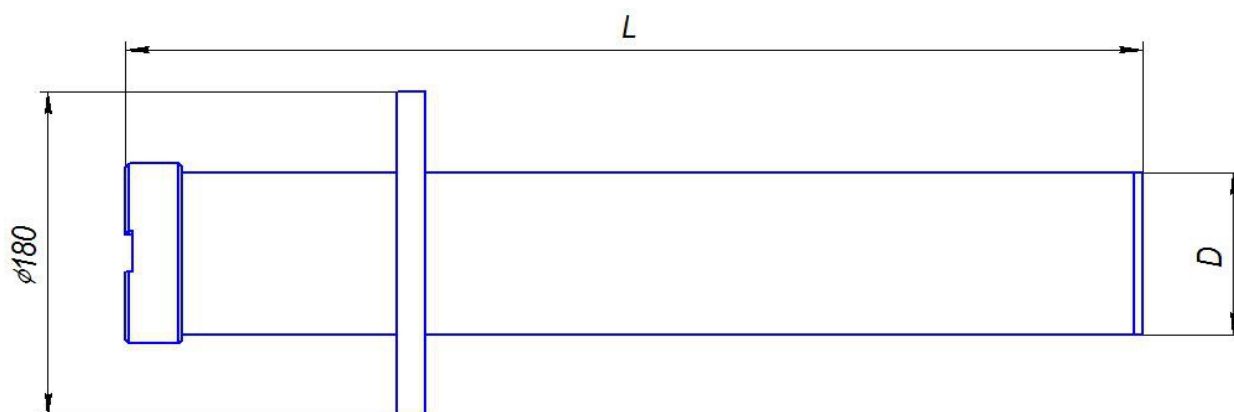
Общий вид и габаритные размеры МОУ-4.
